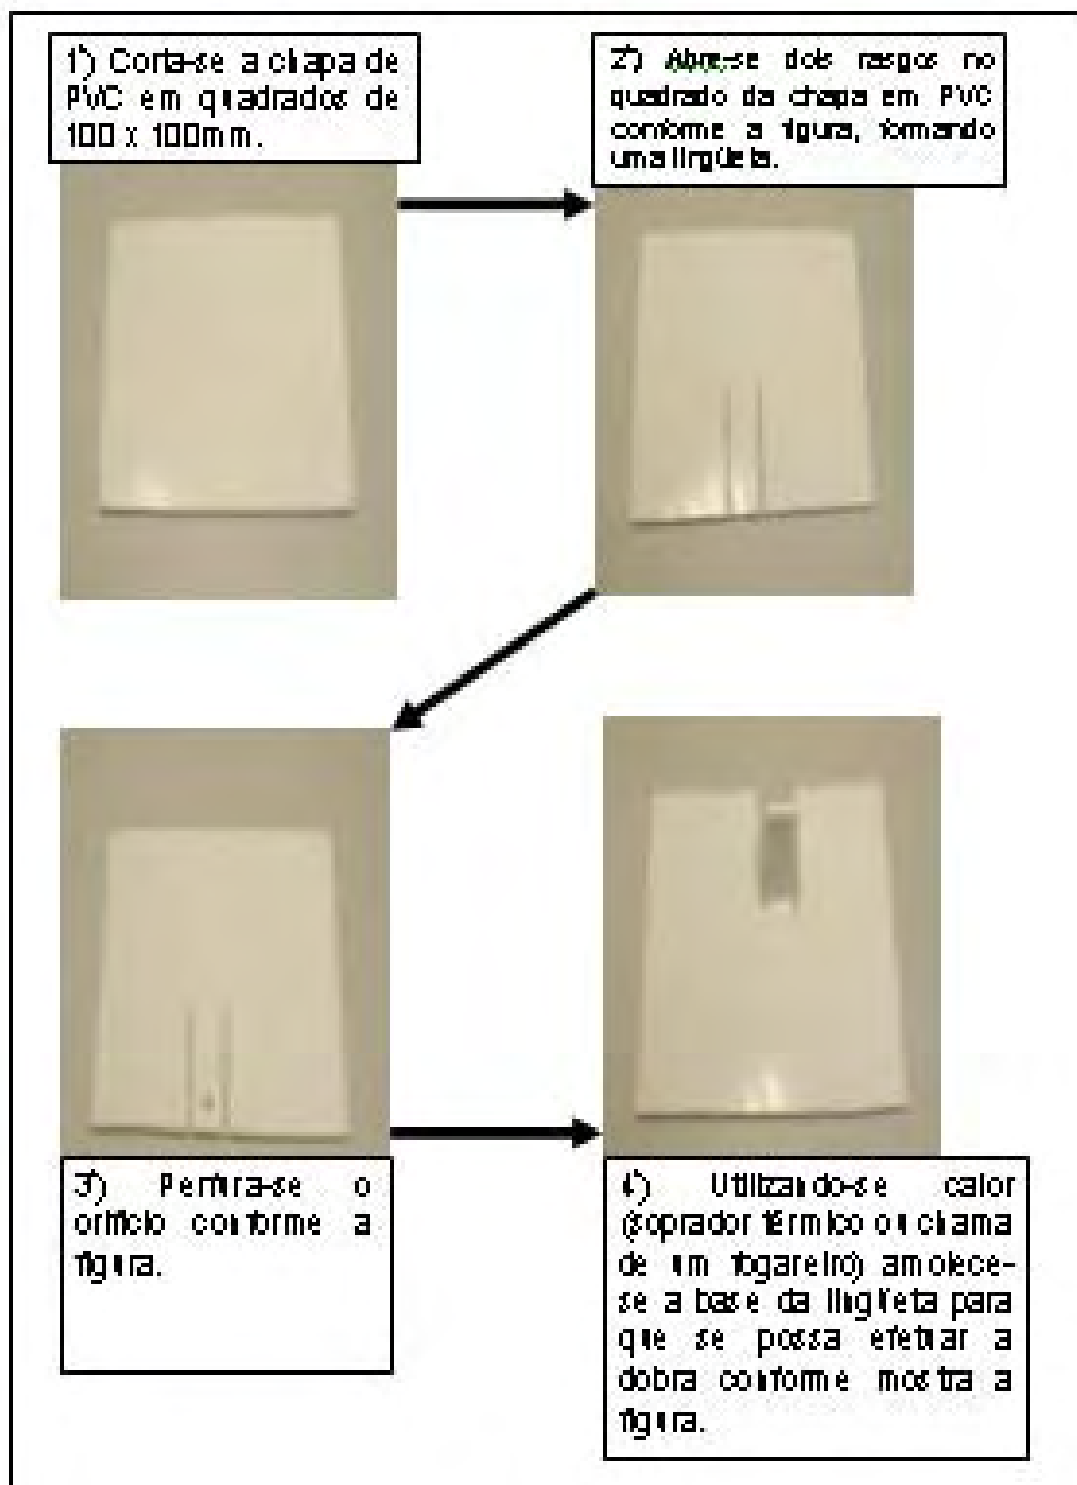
Fotos da sequência de fabricação dos sistemas de fixação das chapas de PVC no concreto armado, para estanqueidade e proteção corrosiva contra o gás sulfídrico presente no biogás.
